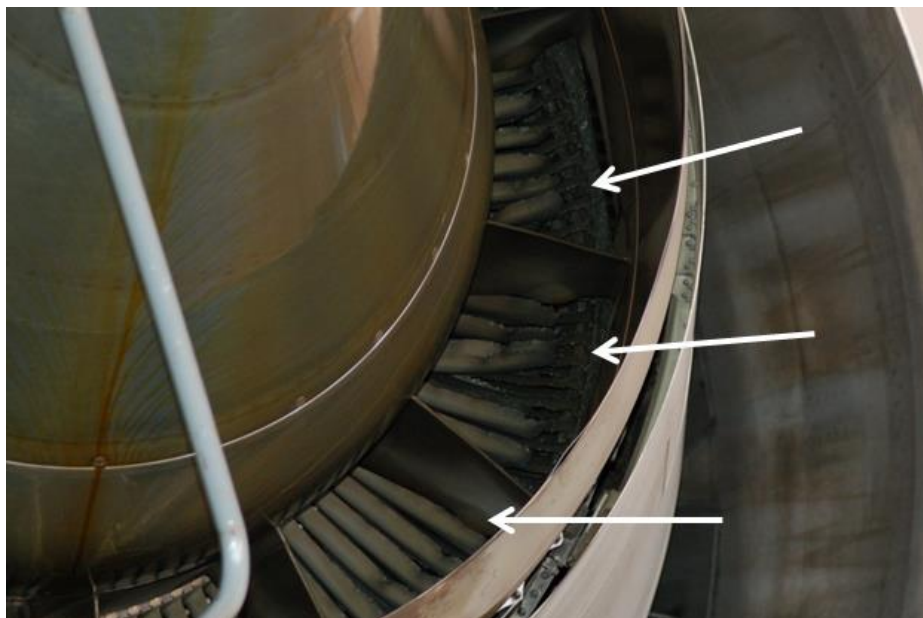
Endommagement des aubes de la turbine BP - section arrière du moteur
